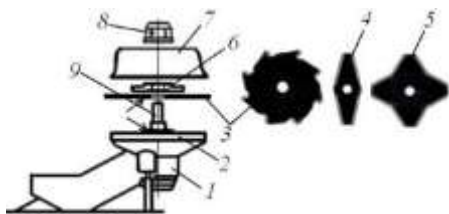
Монтаж рабочих органов кустореза: 1 – корпус редуктора; 2 – поводковый патрон; 3 – режущий орган; 4 – двухлезвийный нож; 5 – 4-х ножевой режущий орган; 6 – нажимной диск; 7 – рабочая тарелка; 8 – гайка; 9 – хвостовик вала с левой резьбой
